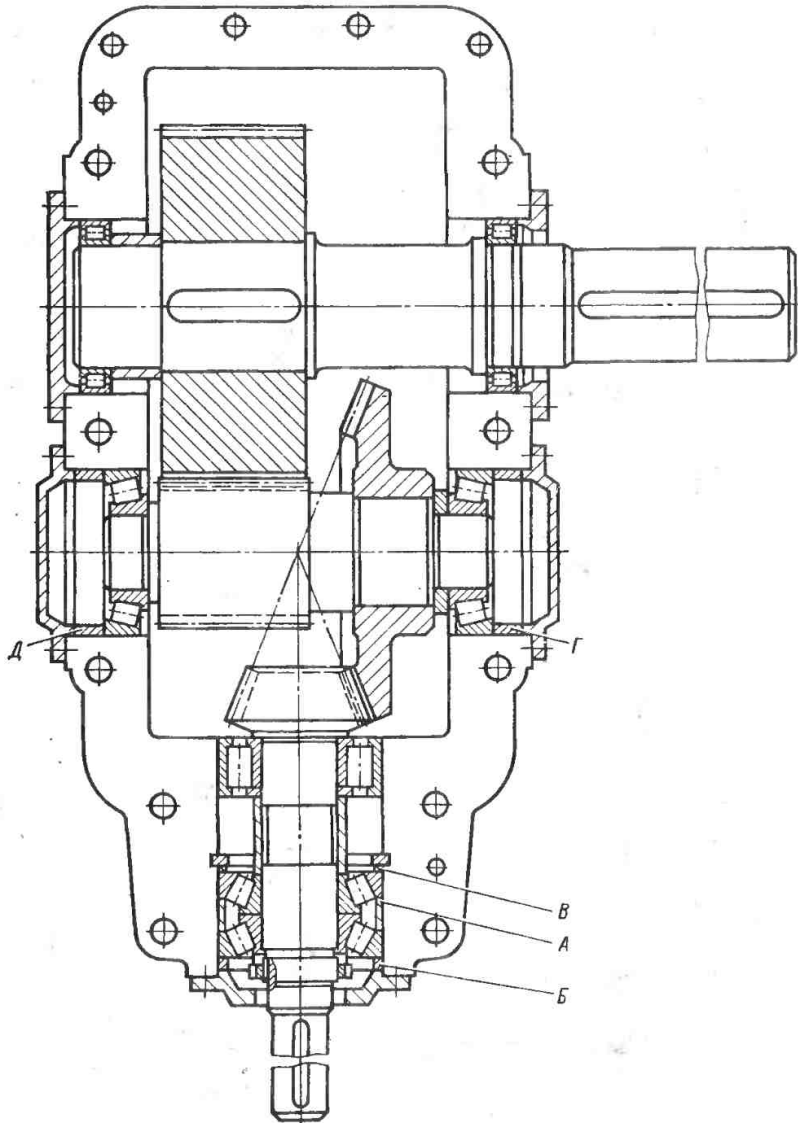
Размещение подшипников качения в зубчатой передаче
